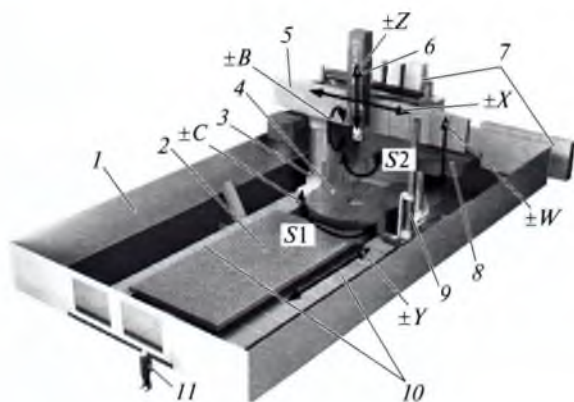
Эскиз станка мод. VMG 50 в масштабе с оператором 11: 1 — ограждение; 2 — стол фрезерной обработки (4,5 × 9 × 3) м; 3 — портал; 4 — стол токарной обработки (диаметр и высота 5 и 3 м); 5 — поперечина портала; 6 — каретка; 7 — шкафы системы управления; 8 — механизм смены инструмента; 9 — терминал оператора с терминалом и выносным пультом; 10 — направляющие портала
